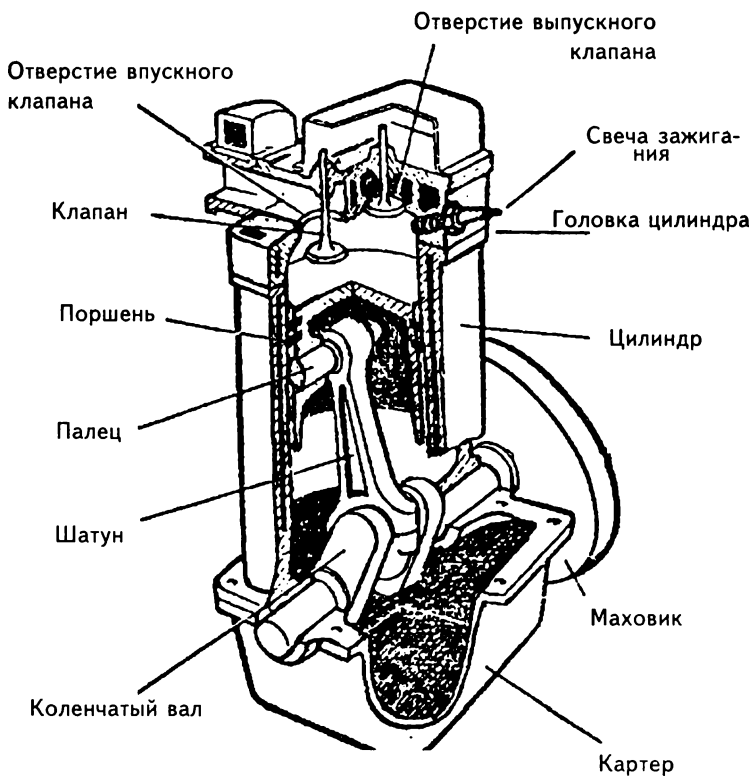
Схема устройства одноцилиндрового поршневого двигателя
